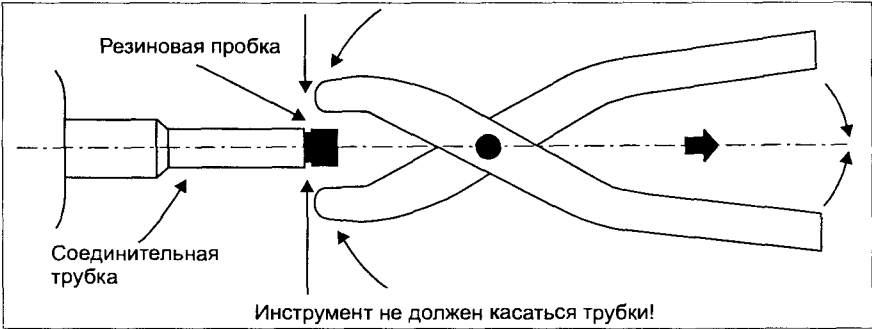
Удаление пробки из соединительной трубки компрессора
